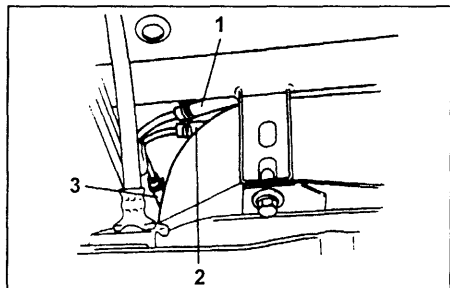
Шланги и патрубки топливного бака. 1 - шланг подачи топлива к карбюратору, 2 - шланг возврата топлива в бак; 3 - шланг вентиляции топливного бака.
